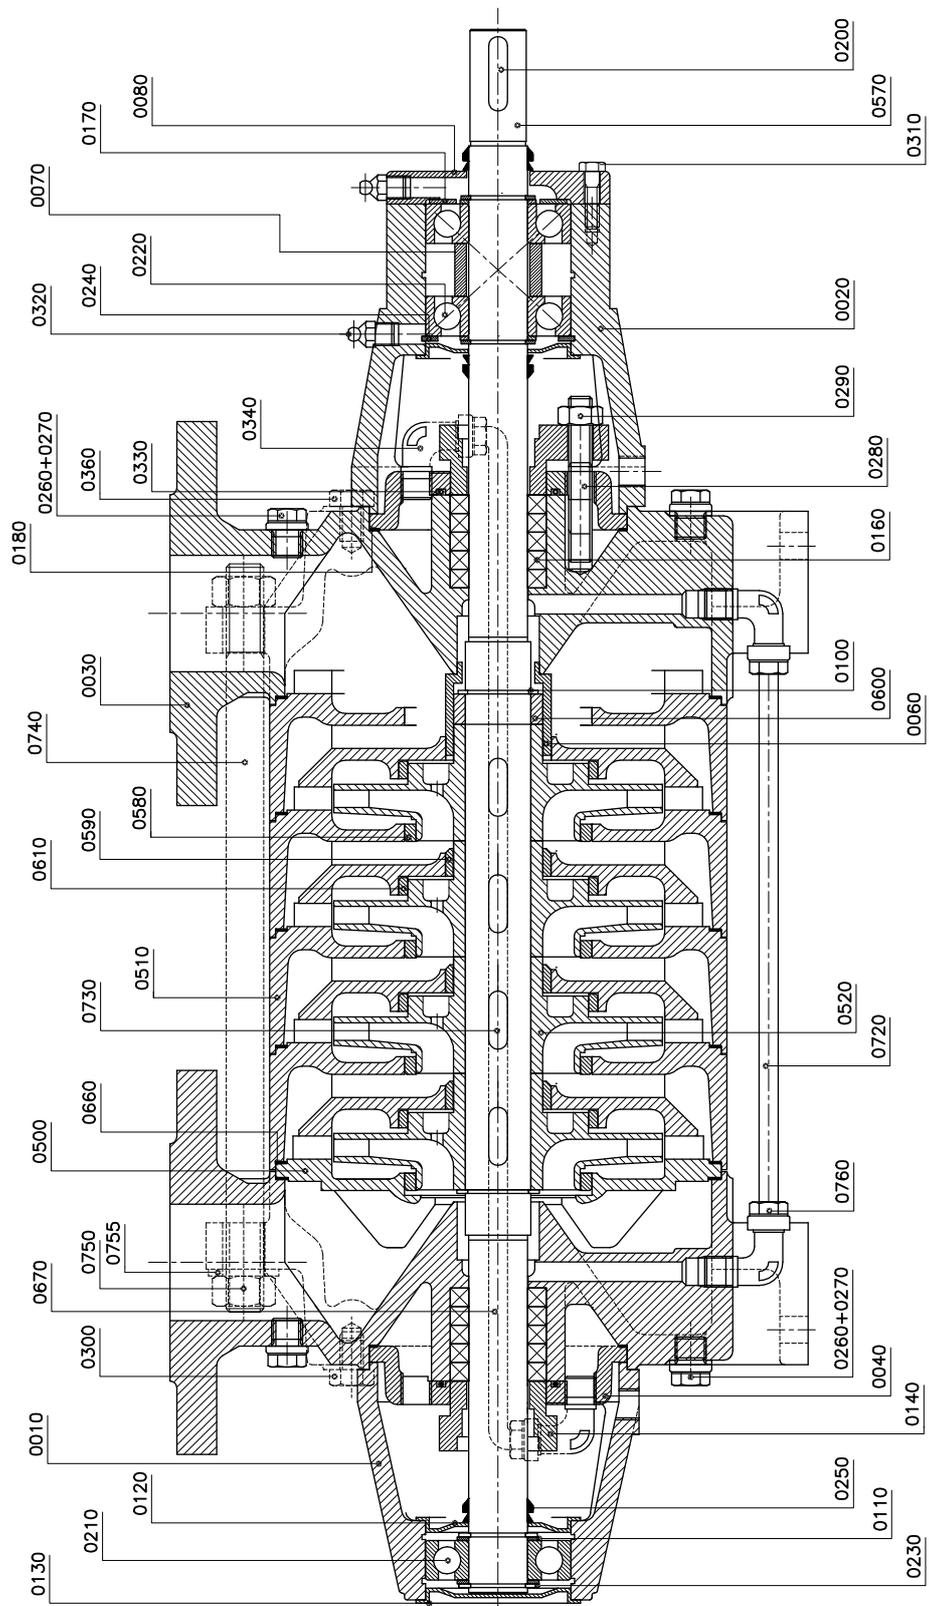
Модель MCHW 14a/b с подшипниками усиленной конструкции.
